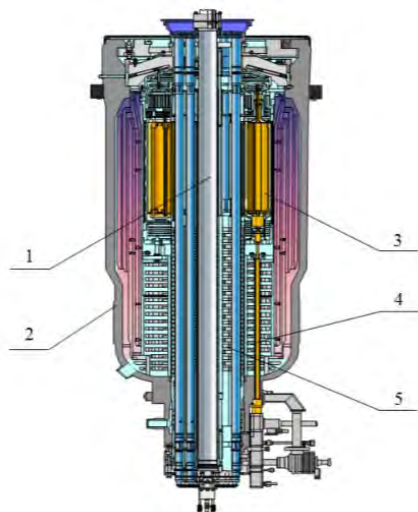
Реактор ИВГ.1М: 1 – центральный канал; 2 – корпус реактора; 3 – регулирующий барабан (РБ); 4 – привод исполнительного механизма РБ; 5 – железобетонная защита
